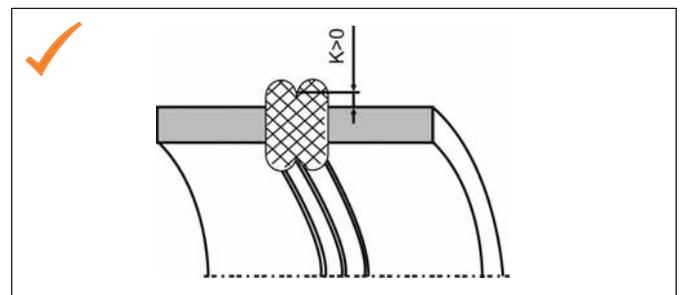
Schnittbild einer guten Schweißnaht
